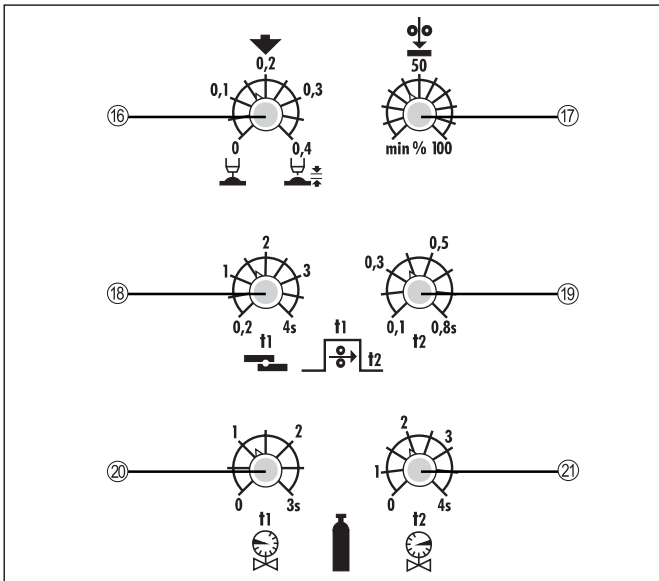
Diverse Einstellregler an der Innenseite des Schweißgerätes
